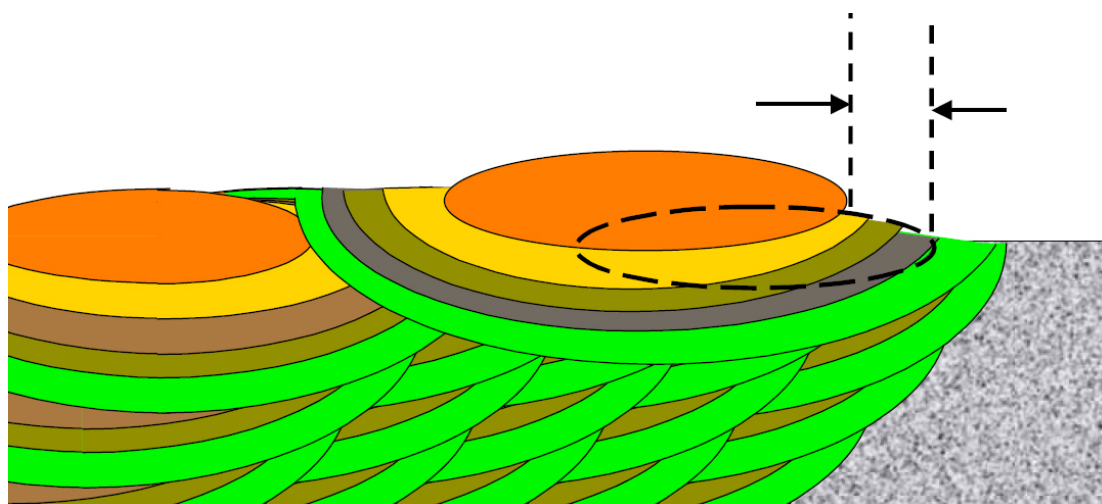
Efeito da deposição de um cordão de solda ao lado de outro
